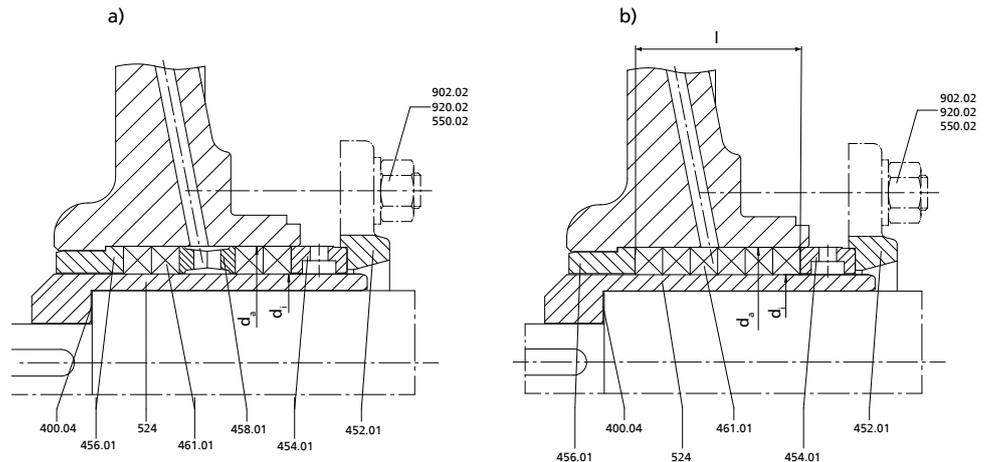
Montar la empaquetadura de prensaestopas a) con anillo de cierre y b) sin anillo de cierre
